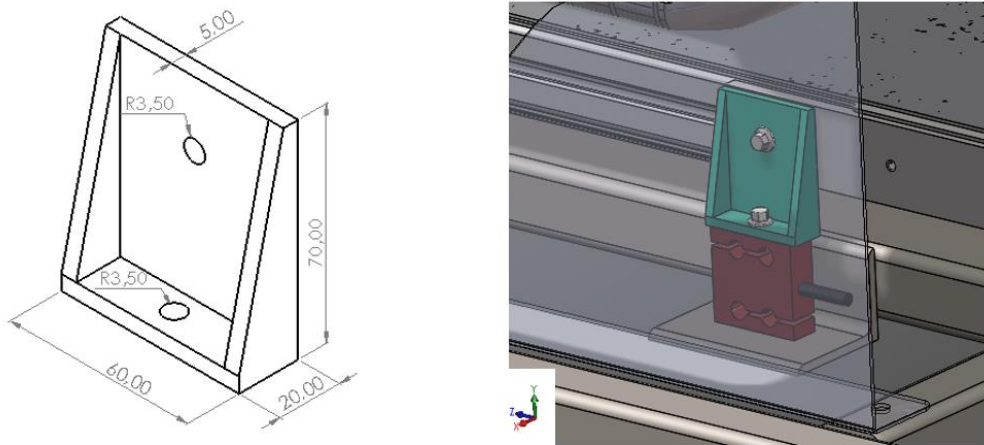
Representação do suporte do tapete transportador (esquerda) e perspetiva em pormenor da montagem do suporte na máquina (direita).
